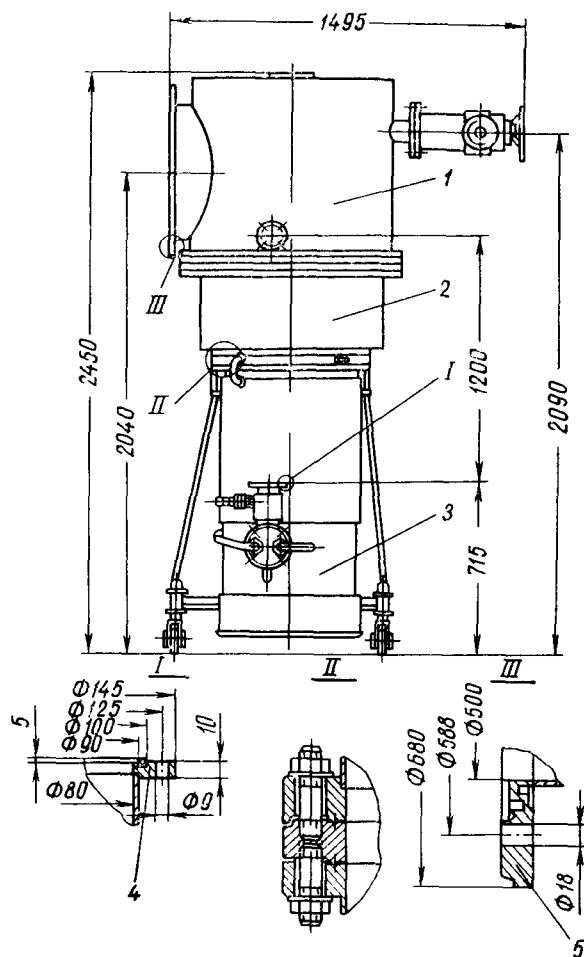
Схема и габаритные размеры агрегата ВА-8-9М:
